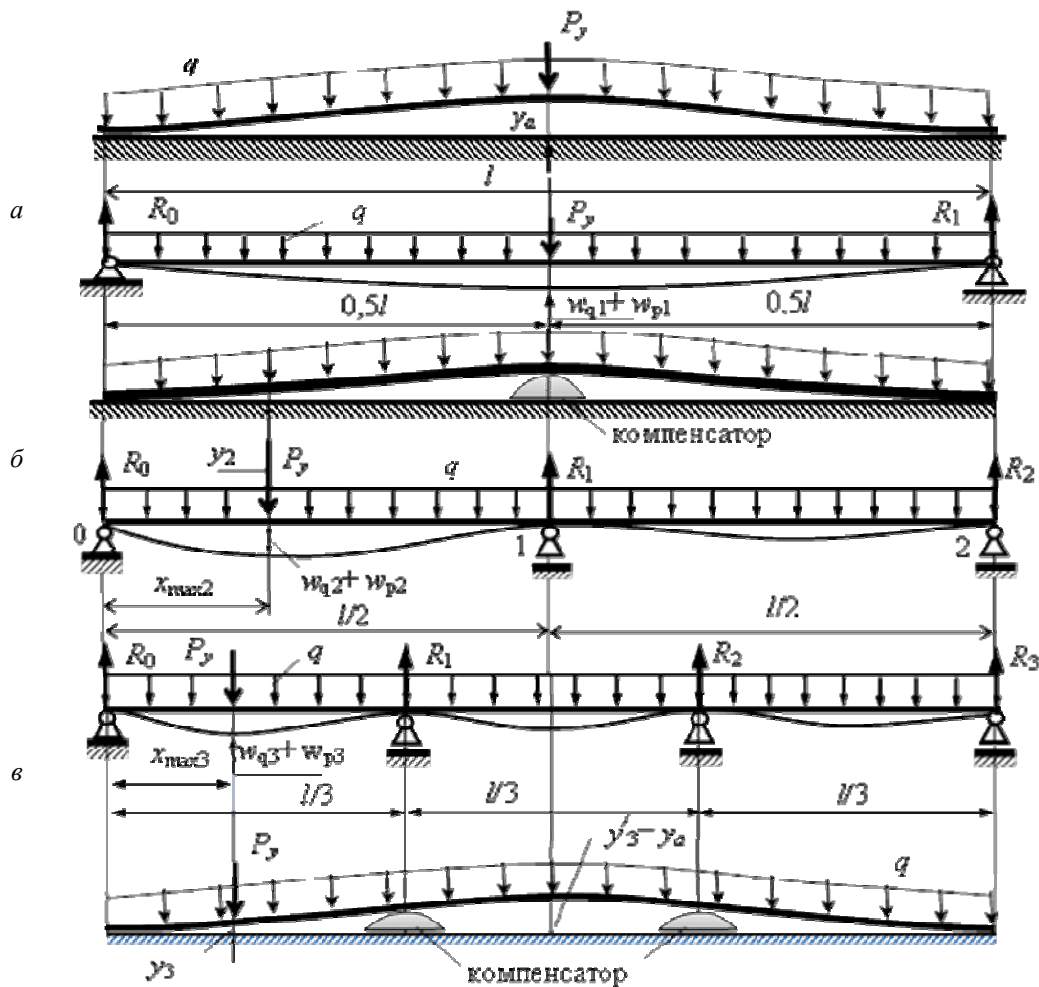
Расчетные схемы заготовки при шлифовании с закреплением магнитным полем стола: а – без компенсаторов; б – с одним компенсатором; в – с двумя компенсаторами
